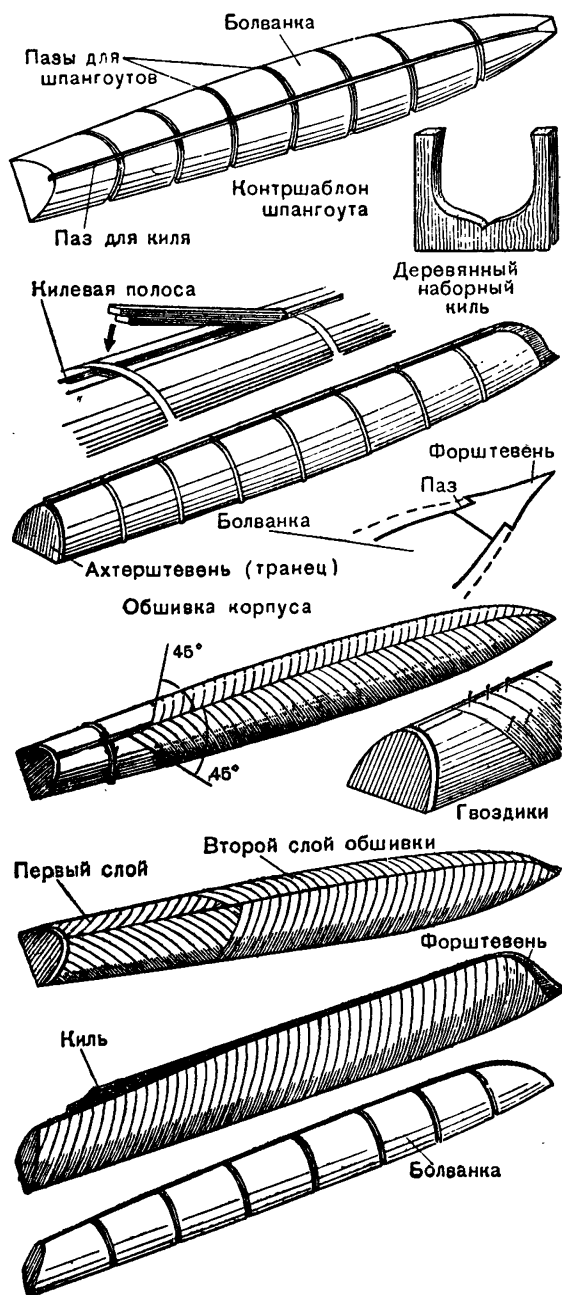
Способ изготовления корпуса модели фанерными полосками на болванке.
